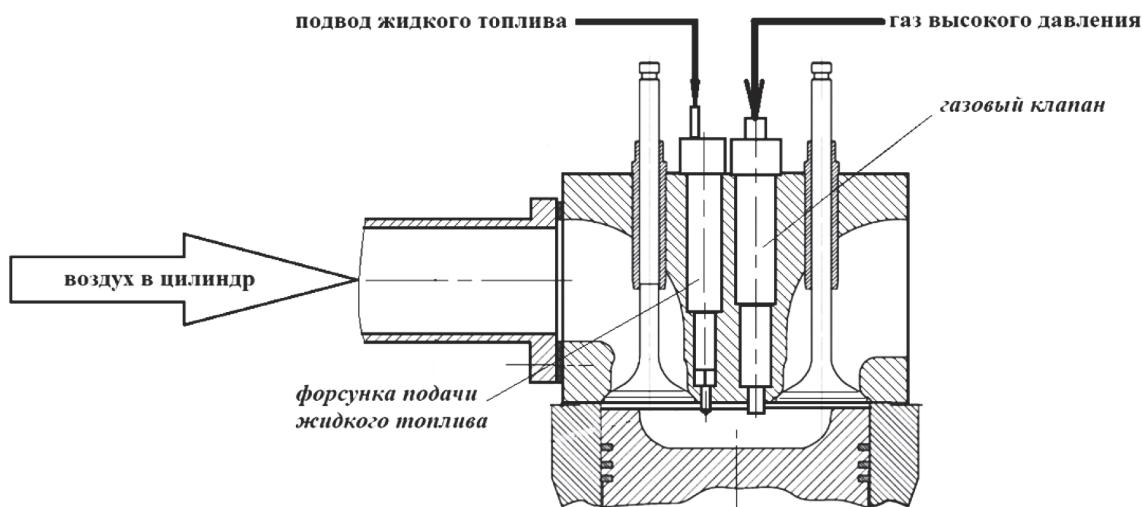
Схема двухтопливного двигателя с газом высокого давления
